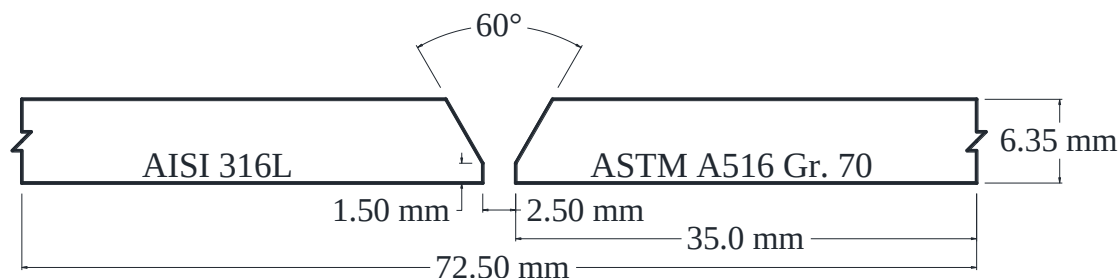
Diseño y dimensiones de la junta disímil con preparación en simple “V”.
